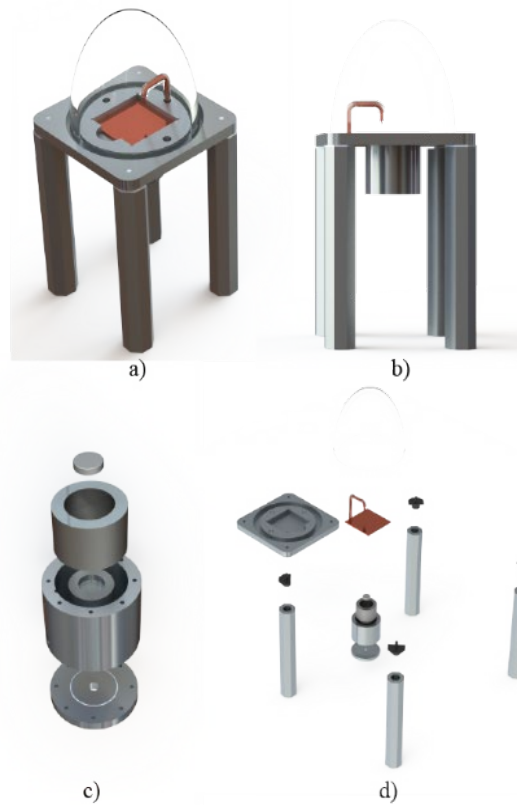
Ensamble del sistema. a) Vista isométrica del prototipo. b) Vista frontal del prototipo.
